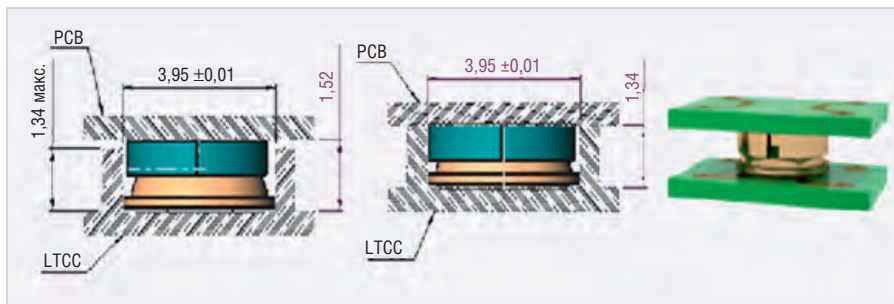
Соединение платы PCB с платой LTCC с помощью соединителя типа R107802000
